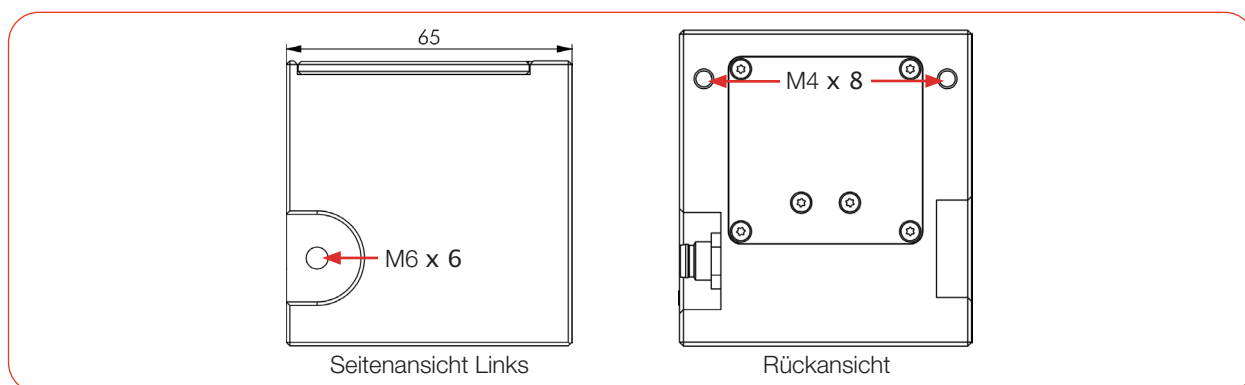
Befestigungsgewinde im Gehäuse (Maße in mm)
